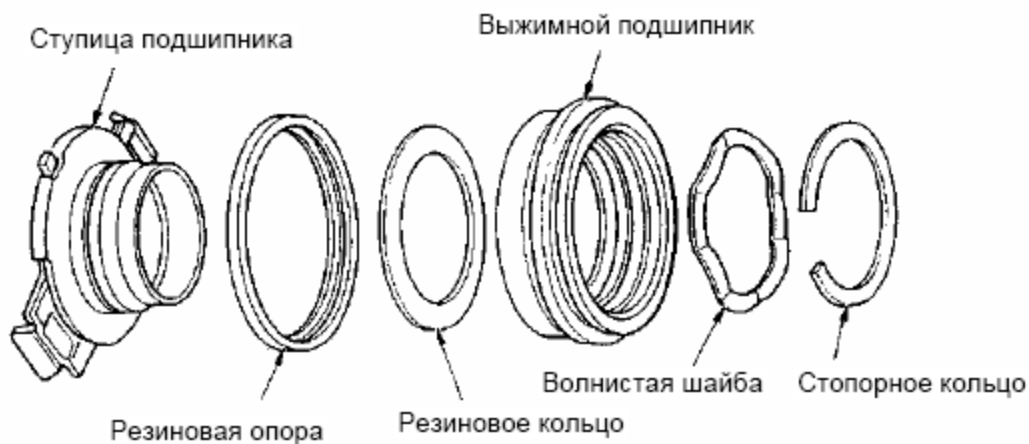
Устройство самоцентрирующего выжимного подшипника
